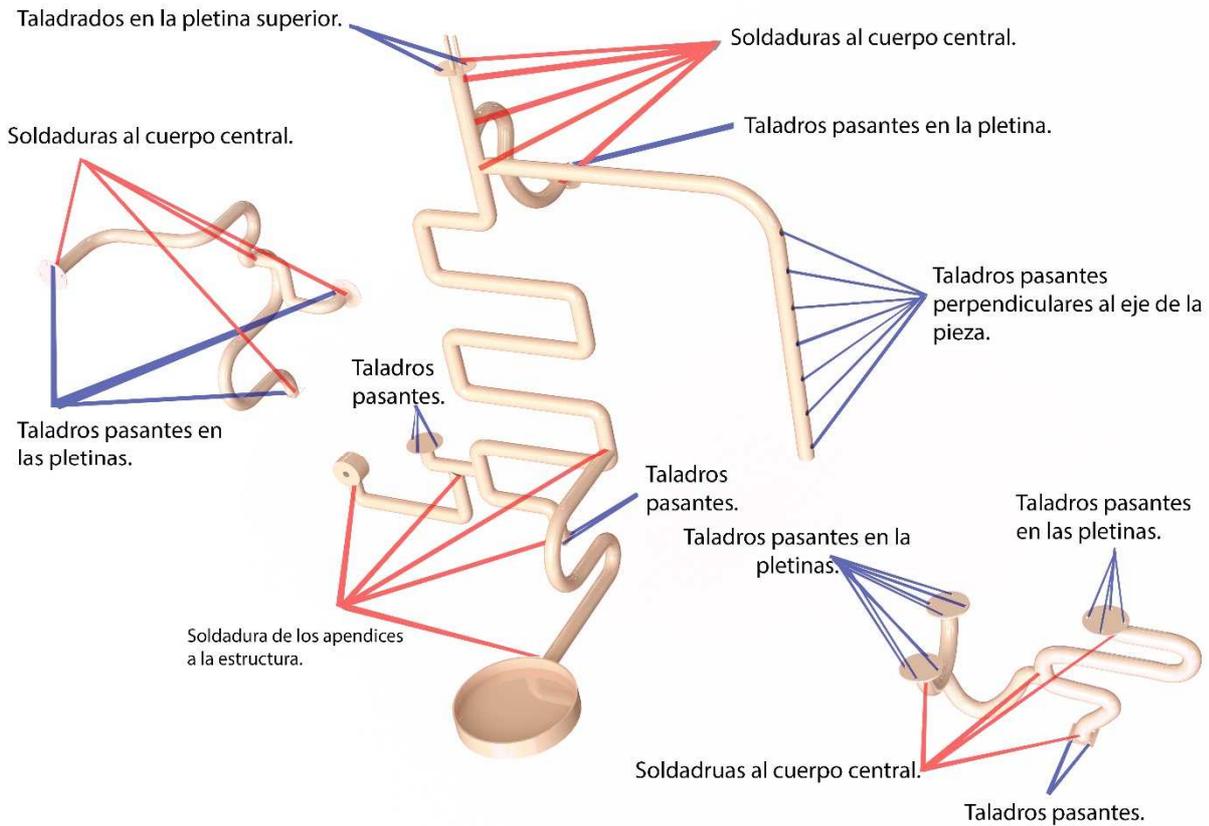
Posiciones de los taladros y las soldaduras en un croquis representativo.
